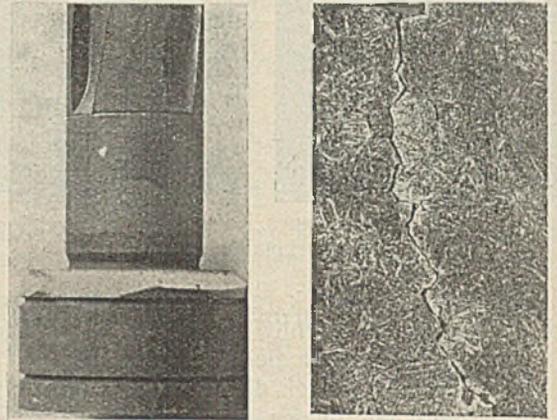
Überhitzter und unsachgemäß gehärteter Kolben mit abgeplatzter Kante.
